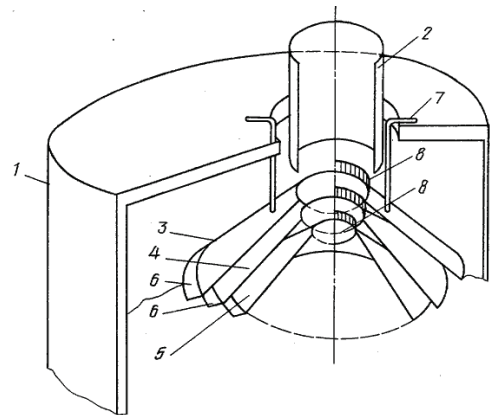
Пристрій для рівномірного завантаження сипких матеріалів: 1 – корпус; 2 – завантажувальний патрубок; 3, 4, 5 – співвісні конуси; 6 – горизонтальні козирки; 7 – кріплення; 8 – обичайки
